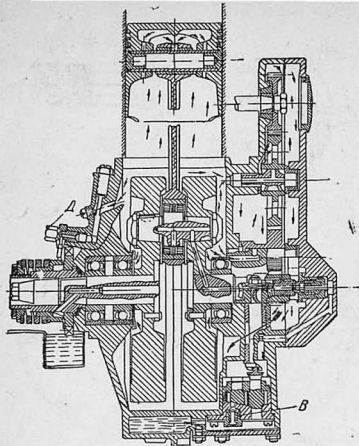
Схема смазки двигателя AM-600 (поперечный разрез). В—перепускной предохранительный клапан; Д—штуцер смазки цепи
